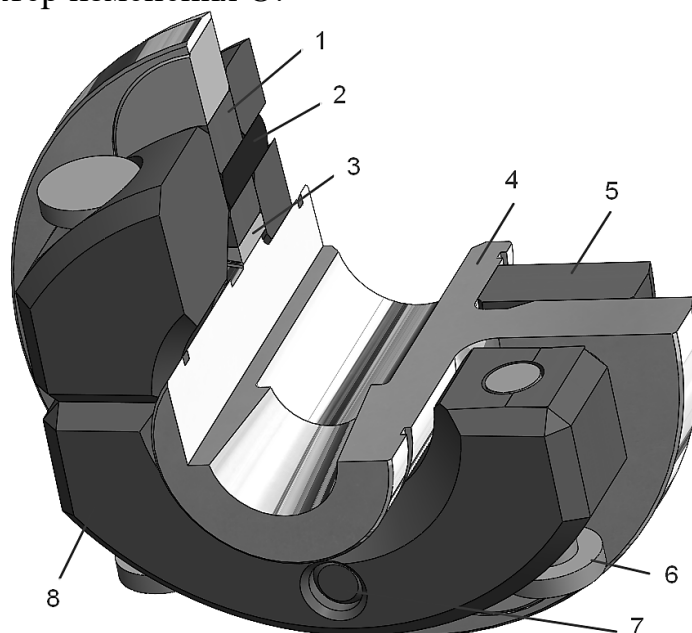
Конструкция АМОВТ: 1 – дополнительный эксцентрик; 2 – палец ведущей полумуфты; 3 – регулировочный эксцентрик; 4 – ведомая полумуфта; 5 – ведущая полумуфта; 6 – палец; груз; 7 – палец регулировочного эксцентрика; 8 - груз.
